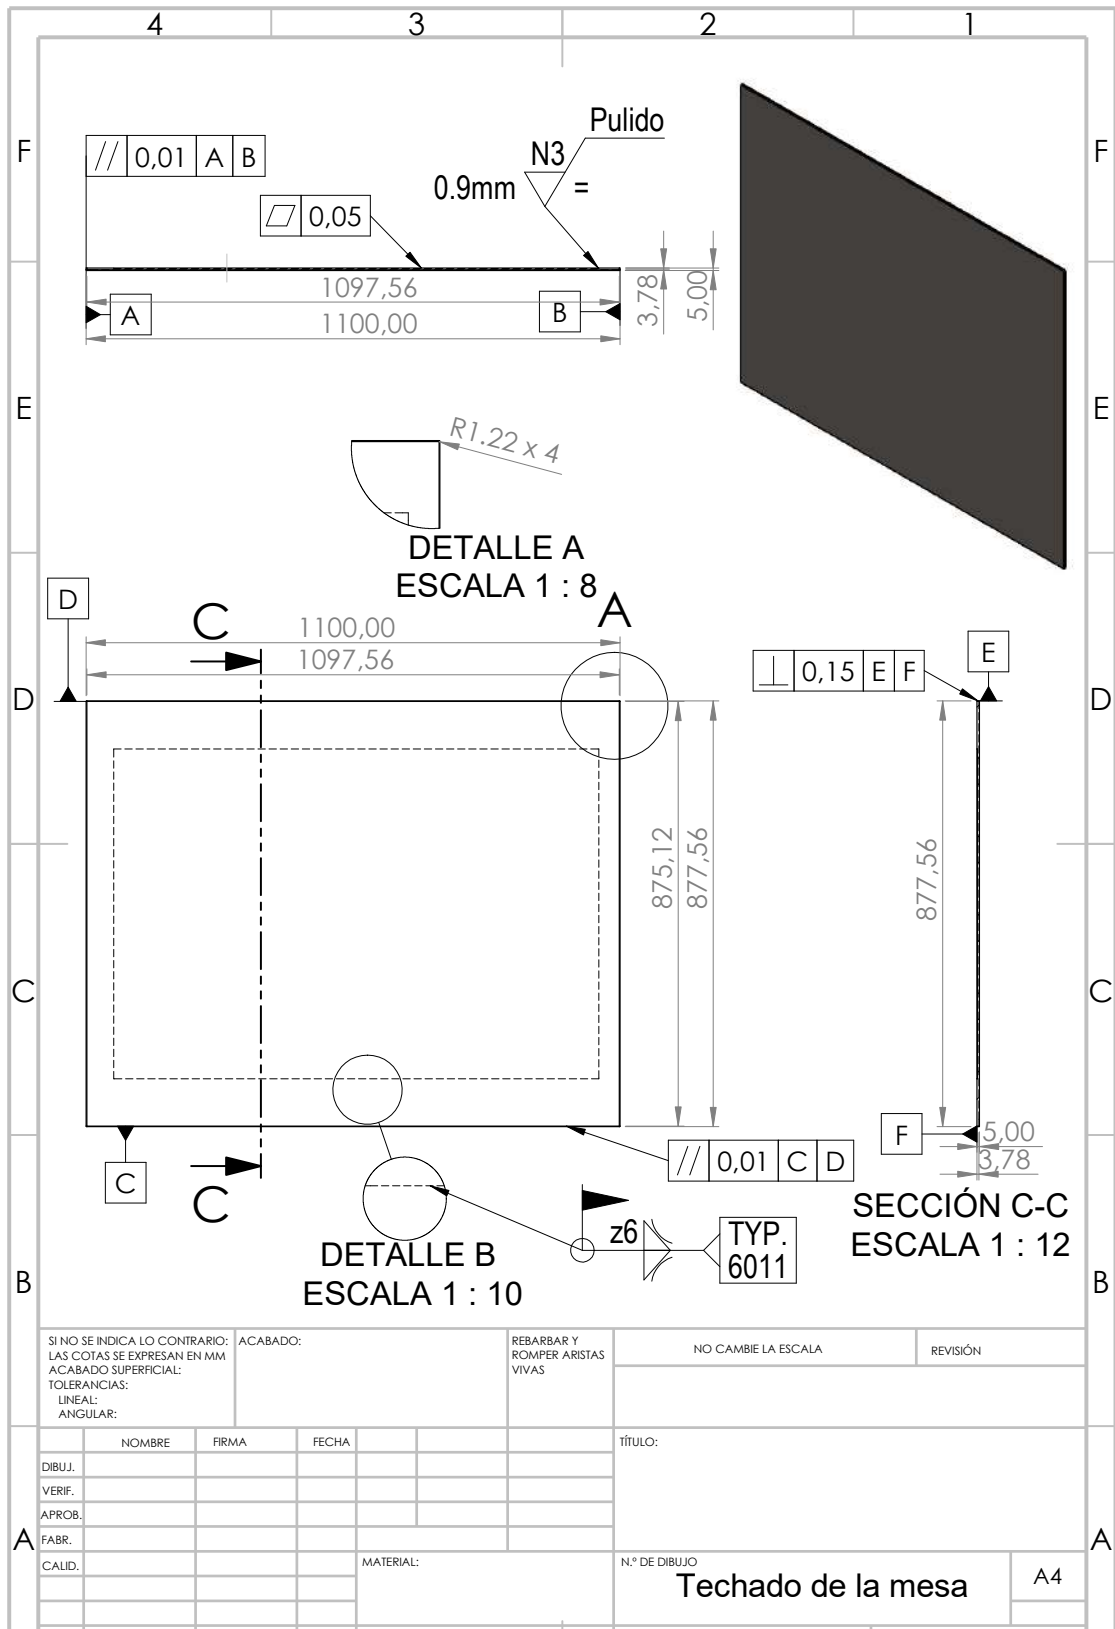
Plano del techado de la mesa. Fuente: Los autores.
